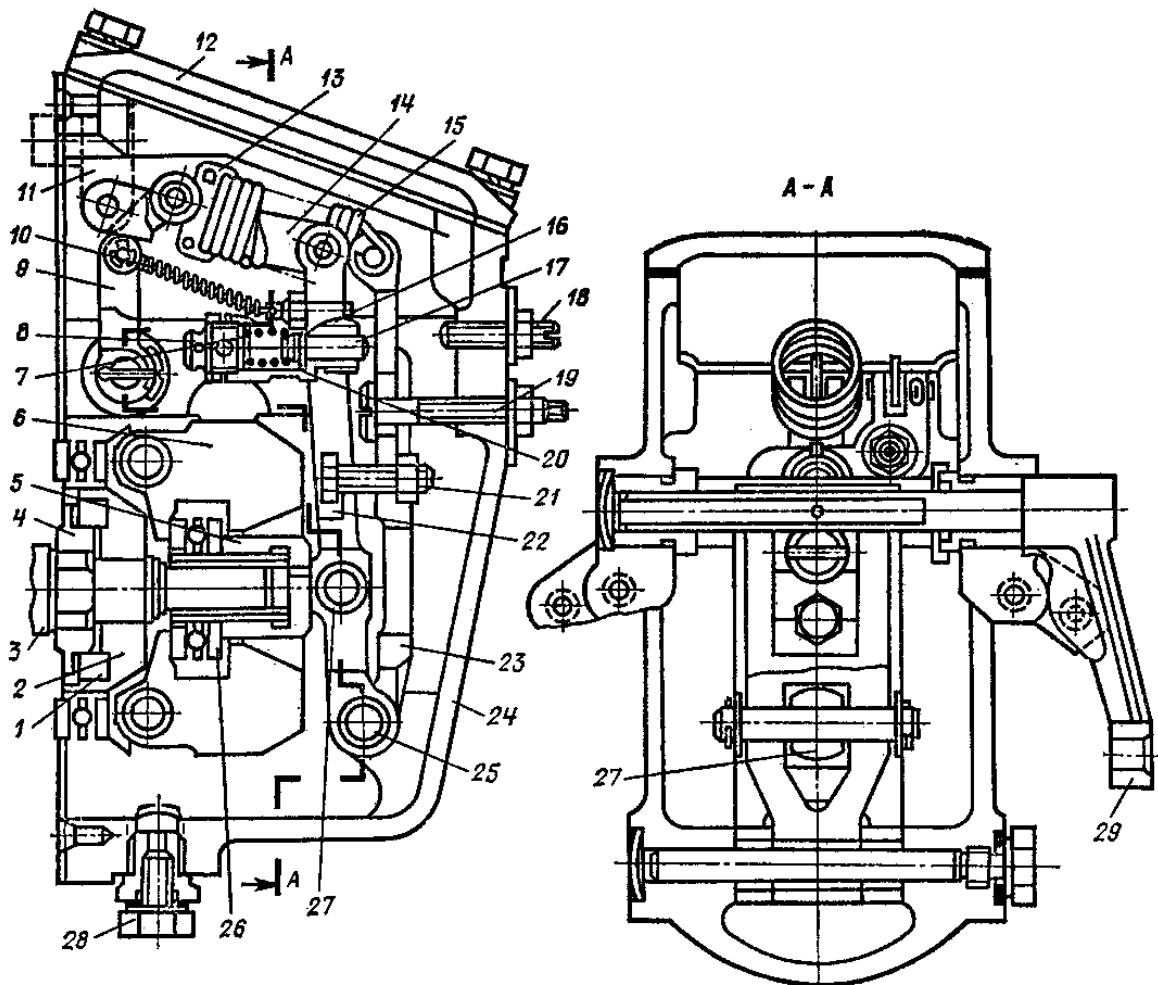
Всережимний регулятор насоса УТН-5: 1 - сухар; 2 - маточина; 3 - кулачковий вал; 4 - упорна шайба; 5 - муфта; 6 - вантаж; 7 - пружина коректора; 8 - гвинт коректора; 9 - важіль пружини регулятора; 10 - пружина пускового збагачувача; 11 - рейка паливного насоса; 12 - кришка; 13 - серга; 14 - тяга; 15 - пружина; 16 - шпилька кріплення пружини збагачувача; 17 - шток коректора; 18 - шпилька; 19 - болт номінальної частоти обертання колінчастого вала; 20 - корпус коректора; 21 - болт; 22 - проміжний важіль; 23 - основний важіль; 24 - корпус регулятора; 25 - вісь; 26 - упорний кульковий підшипник; 27 - бочкоподібний ролик; 28 - зливна пробка; 29 - важіль керування
